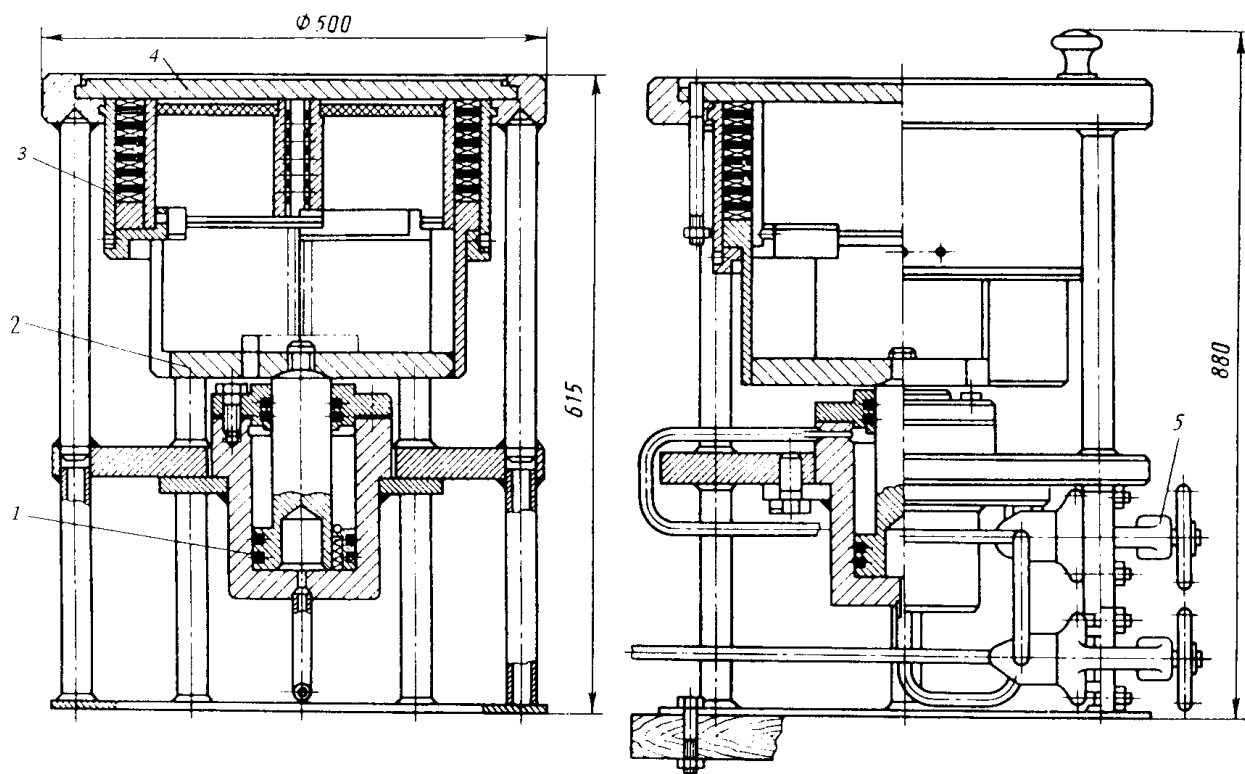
Приспособление для прессования сальниковых колец арматуры
